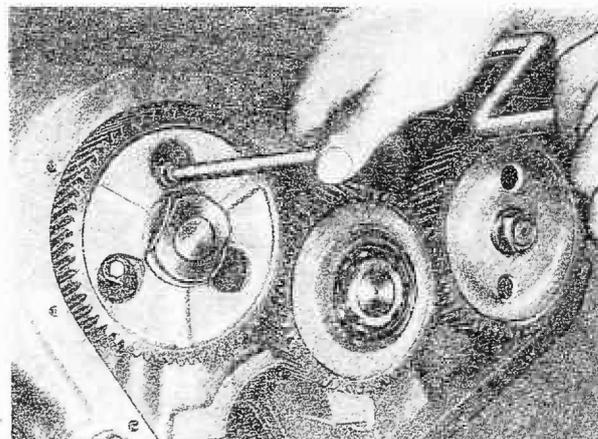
Befestigungsschrauben der Anlaufscheibe lösen
